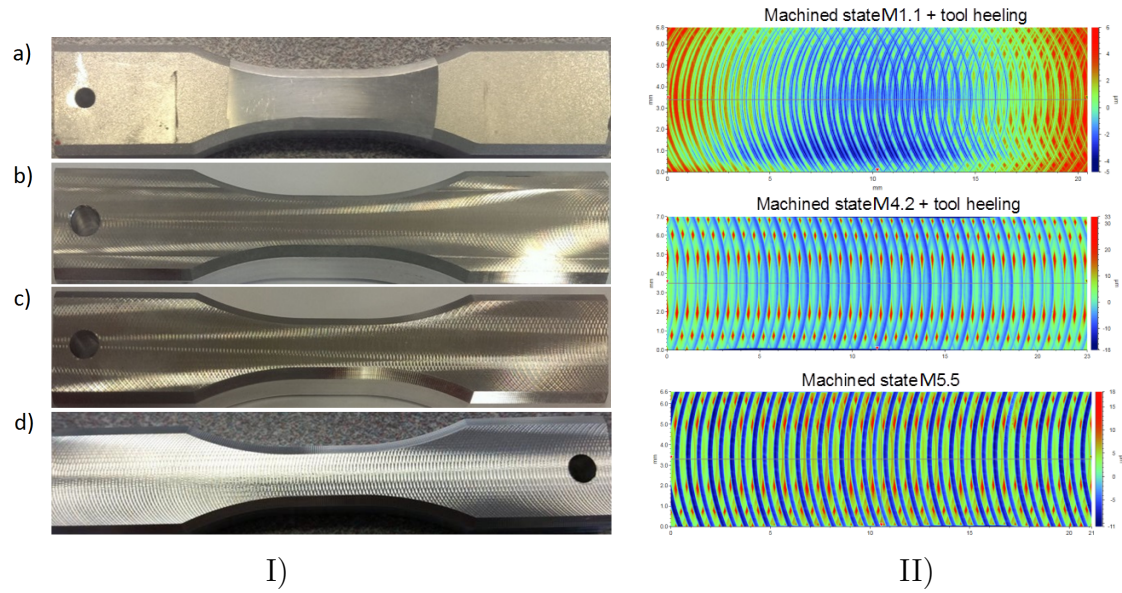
I) Photos des éprouvettes, II) Scan profilométrique associé aux éprouvettes usinées en condition : b) optimale, c) dégradée M4.2 et d) dégradée M5.5.
